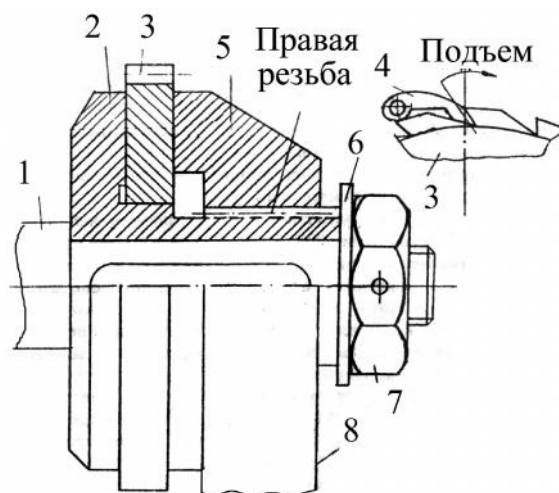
Винтовой тормоз: 1 – вал; 2 – упорный диск; 3 – храповик; 4 – собачка; 5 – диск-гайка (ступица приводной звездочки); 6 – шайба; 7 – гайка; 8 – приводная звездочка
